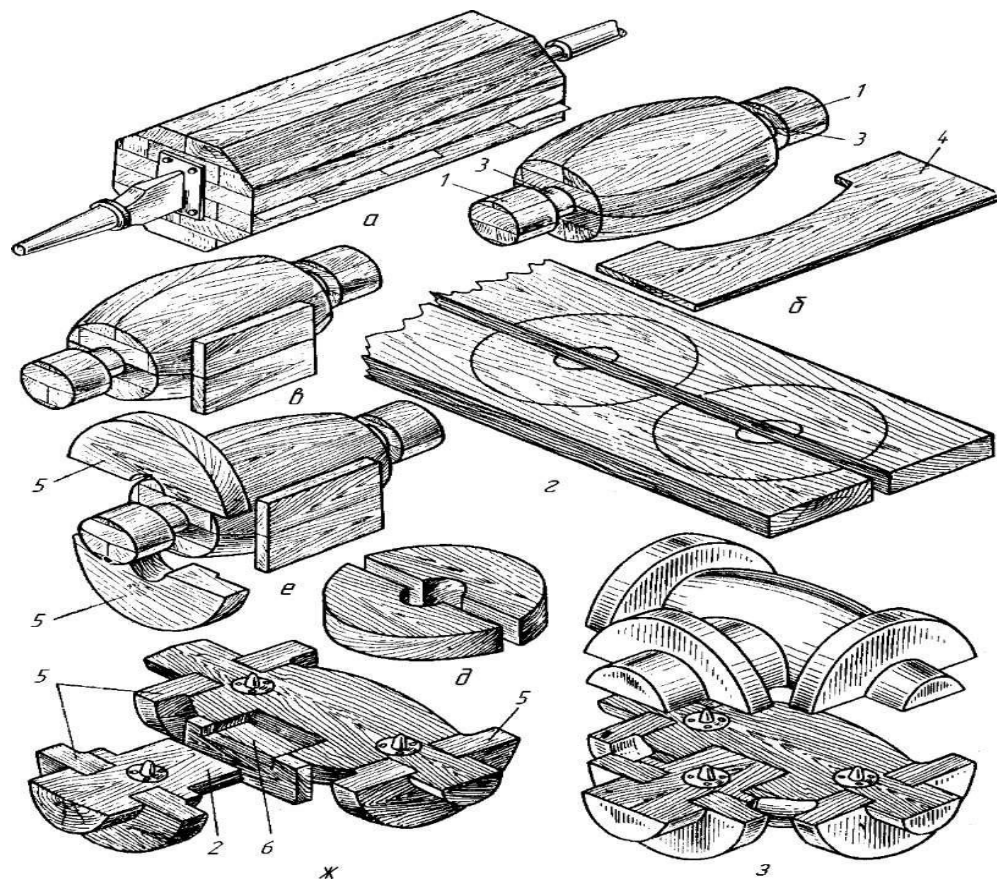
Процесс изготовления модели «Корпуса вентиля»
